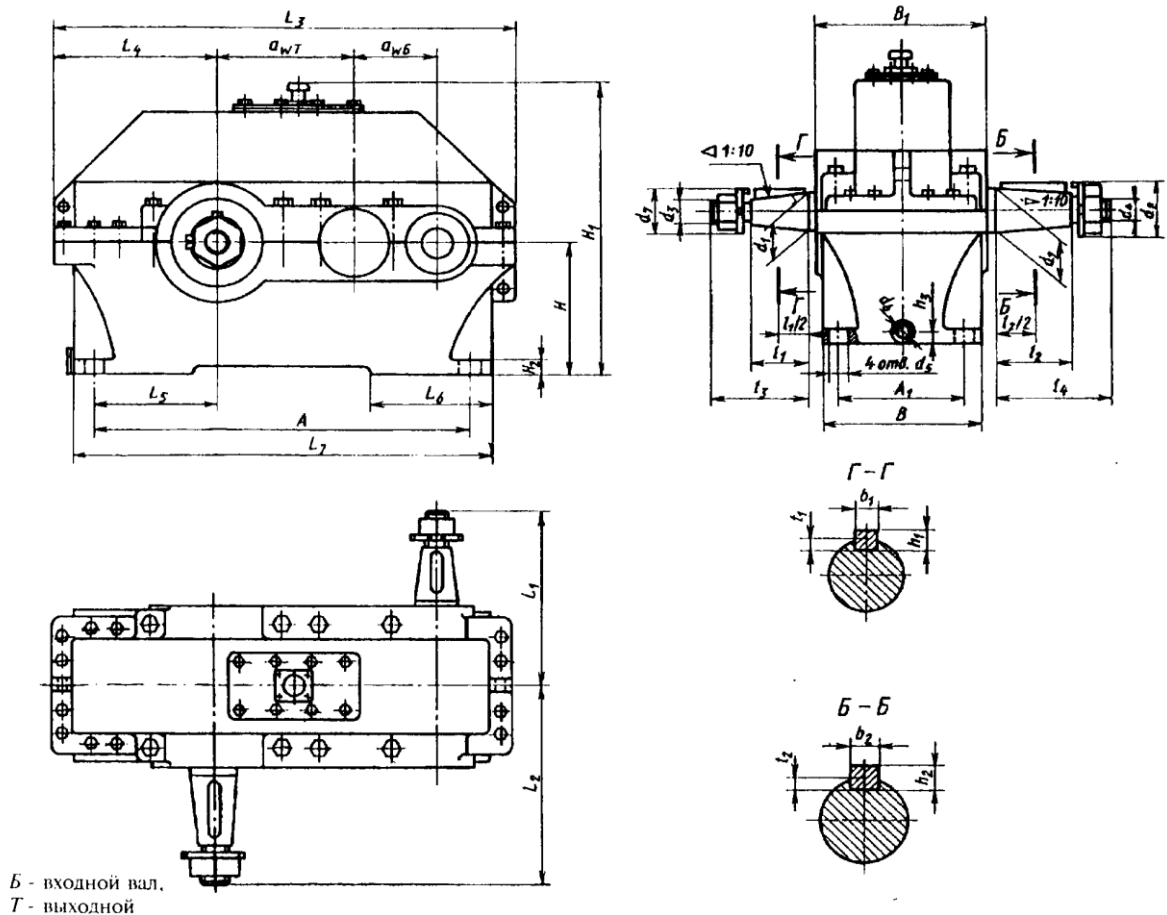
Цилиндрический двухступенчатый редуктор Ц2У-160
